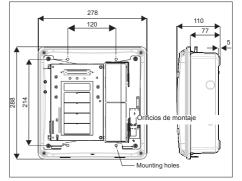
Vista dimensional del Gasmaster con sus orificios de montaje
